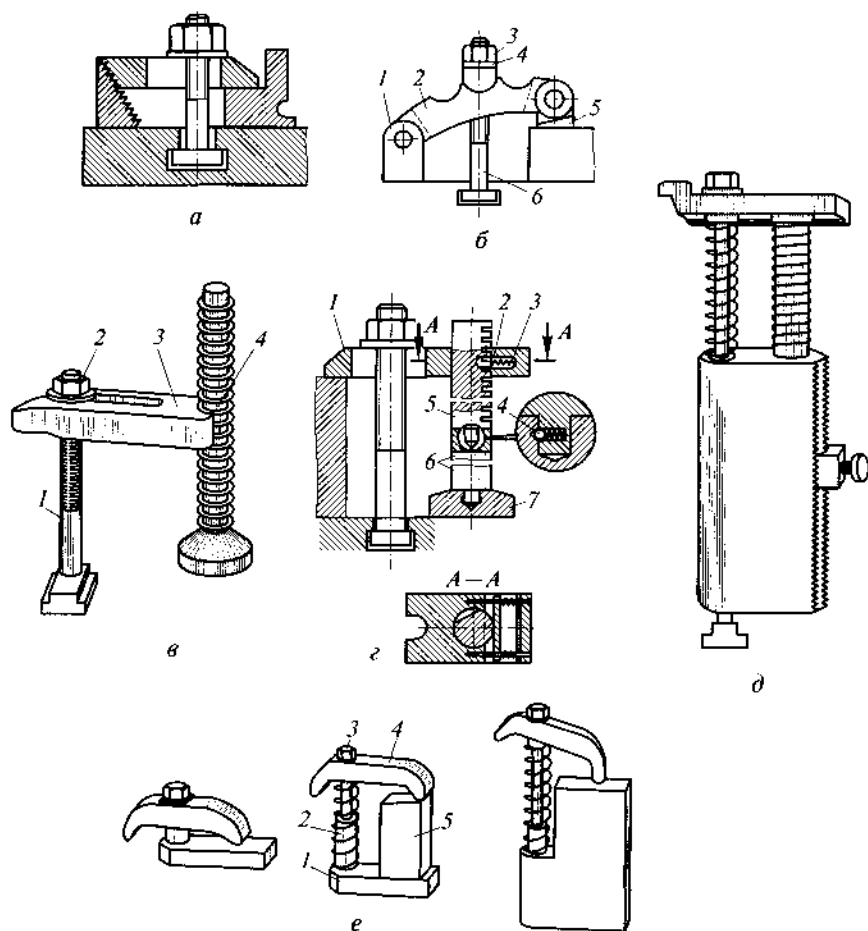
Зажимные устройства для вертикального закрепления заготовок:
